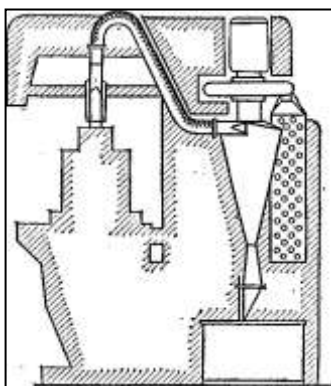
Оборудование фрезерного станка для удаления из зоны резания стружки и пыли
